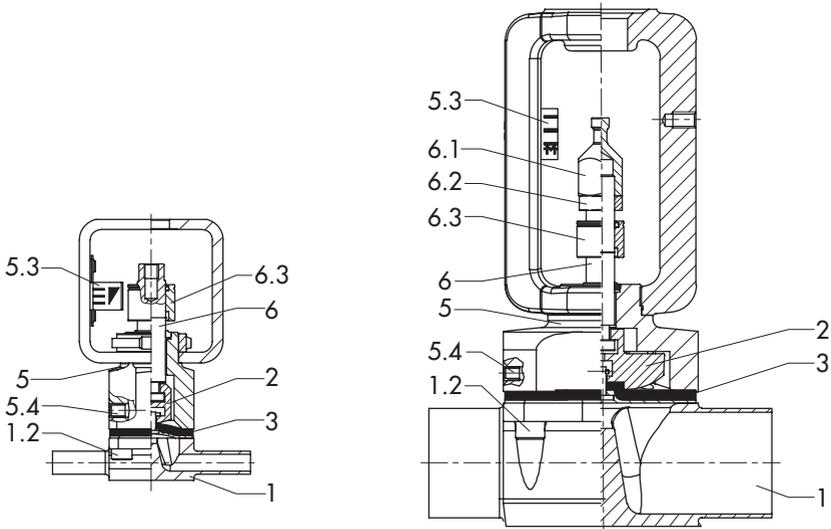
Niro-Ausführung für Antrieb 120 cm² (links) und Sonderausführung für Lebensmittelindustrie in DN 32 bis 100 (rechts)
